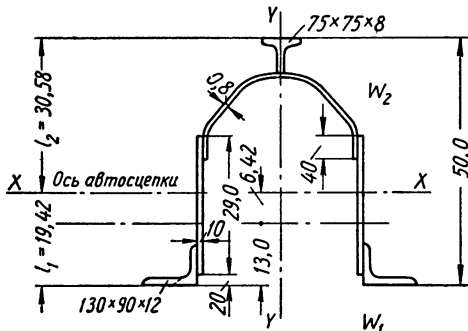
Верхняя накладка хребтовой балки 60-тонной гондолы типа 1941 г.
